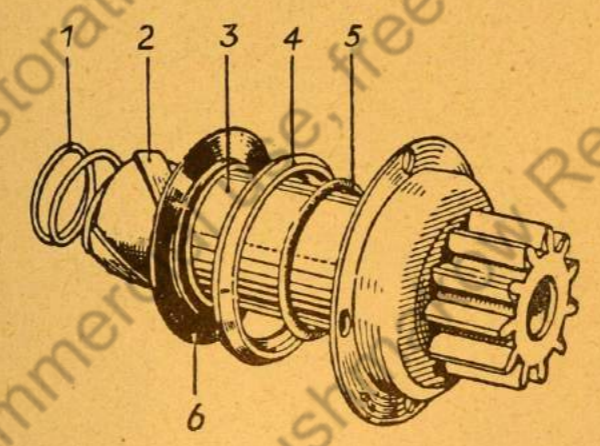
Aufbringen der Simmerring-teile auf den Rißelschaft
